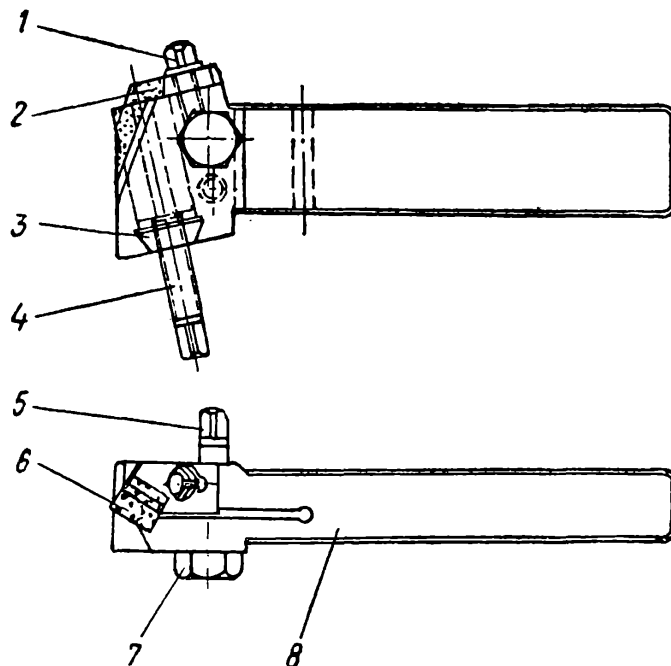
Многолезвийный расточной резец с квадратной вставкой:
